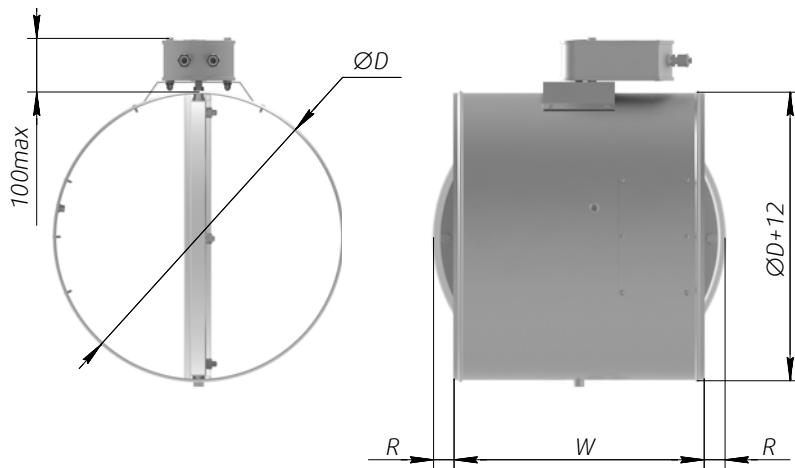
б. Размеры дымового ниппельного клапана HELMER, E60 (90)
